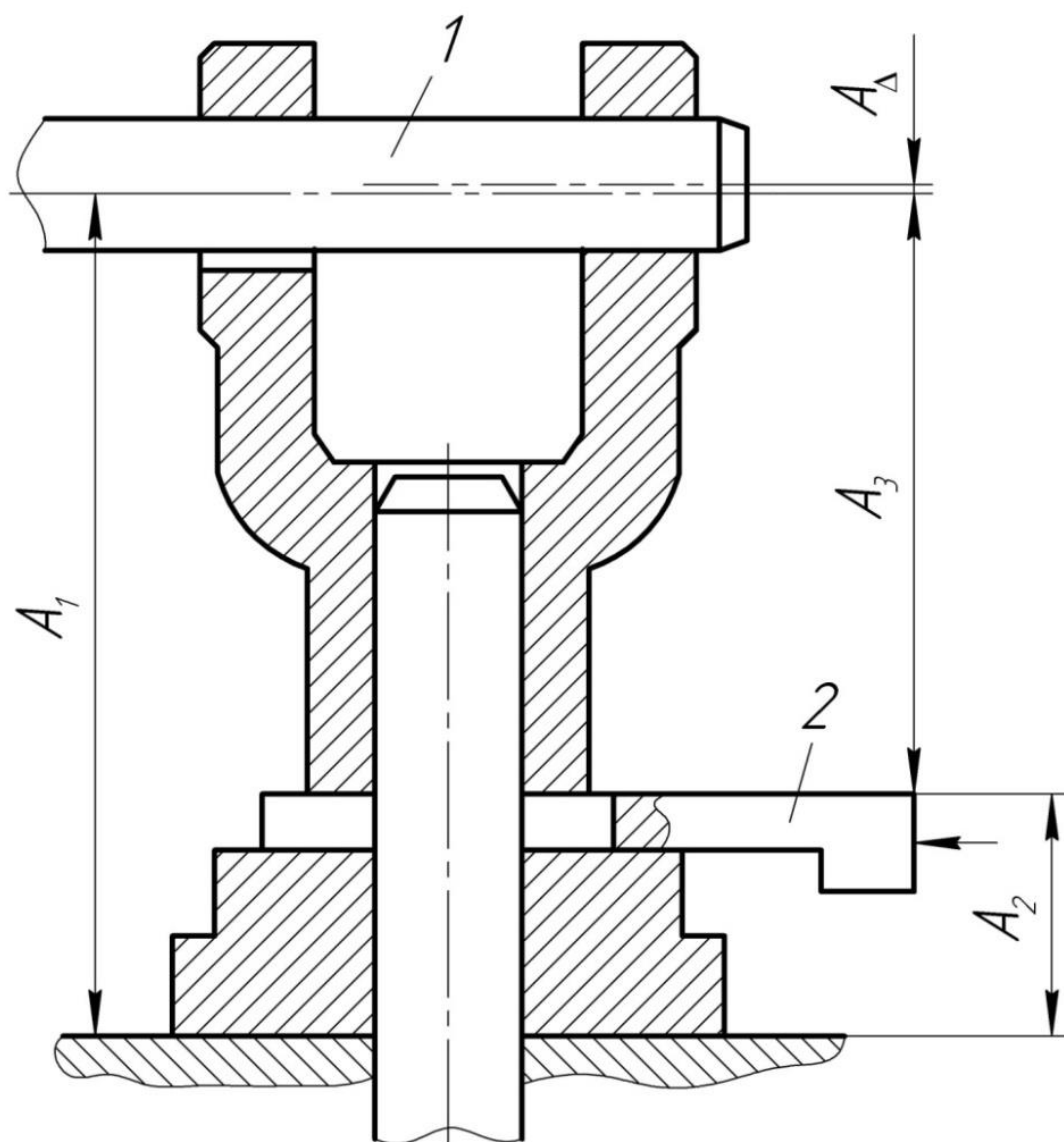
Схема базирования вилки кардана для сборки с крестовиной и подшипниками
